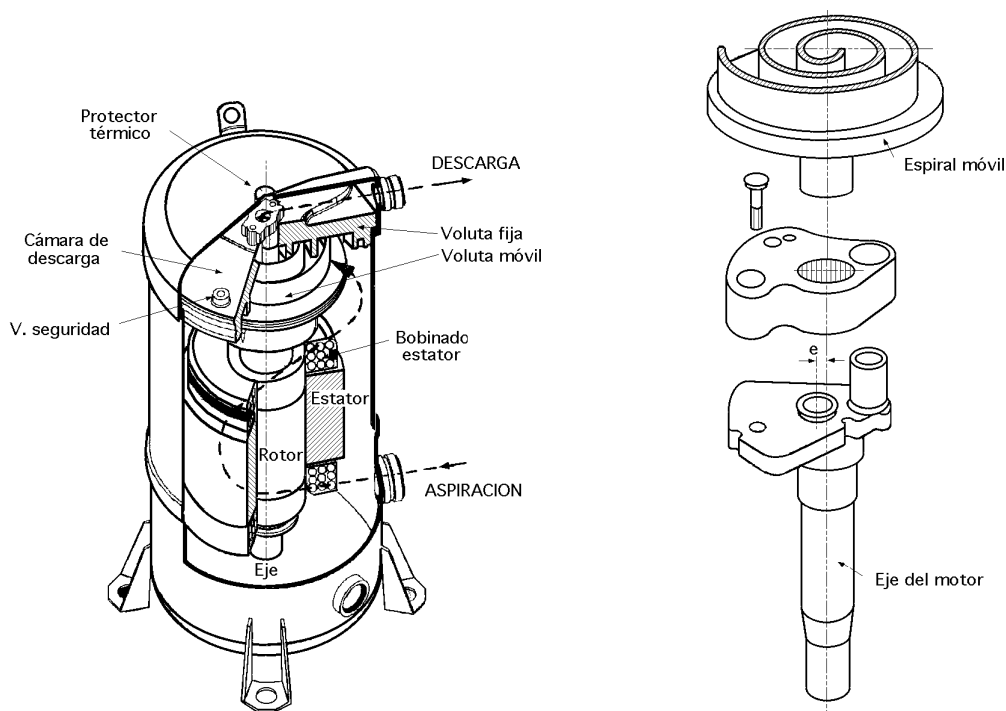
Vista del conjunto árbol motor-rotor del compresor Scroll, y conjunto espiral móvil-eje del motor
